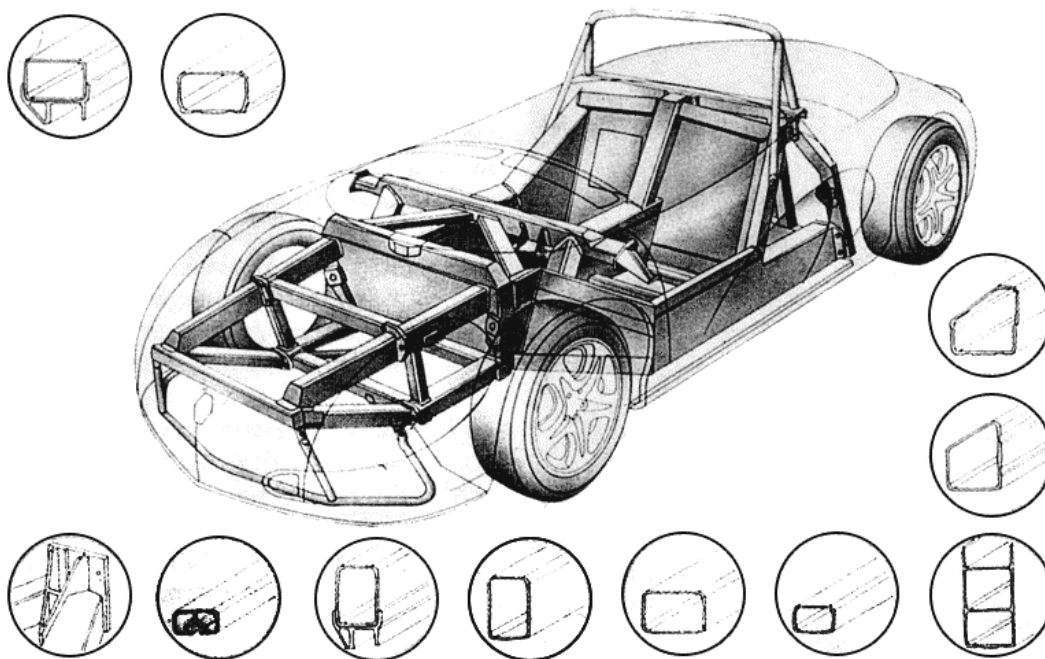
Struttura dello Space Frame e sezioni dei profilati - Renault Spider
